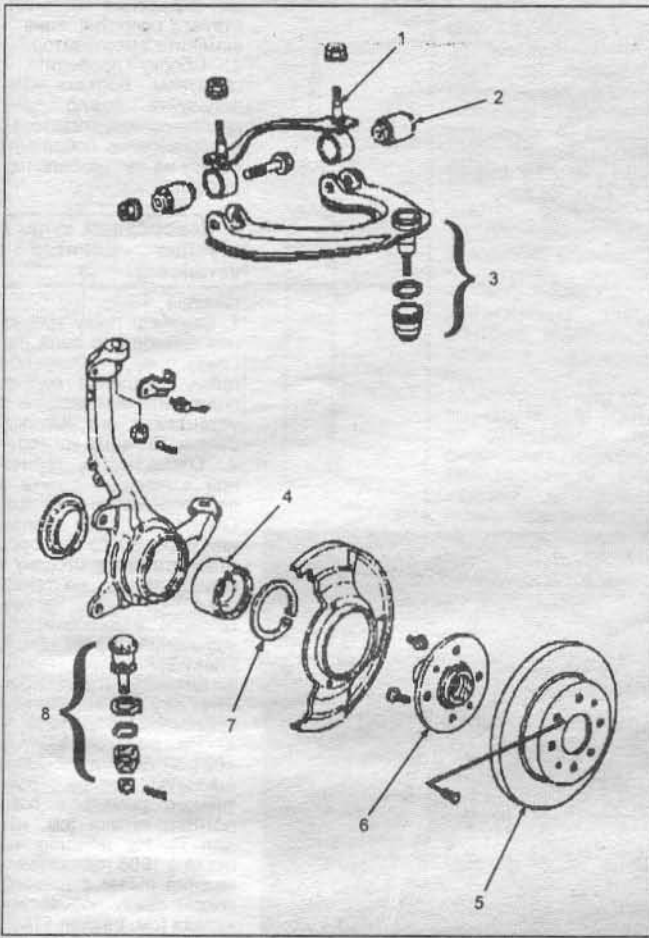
Элементы передней подвески (модели с 1988 г.): 1 - крепление верхнего рычага; 2 - сайлент-блок; 3 - верхняя шаровая опора; 4 - подшипник ступицы; 5 - тормозной диск; 6 - ступица; 7 - стопорное кольцо (75 мм); 8 - нижняя шаровая опора.
